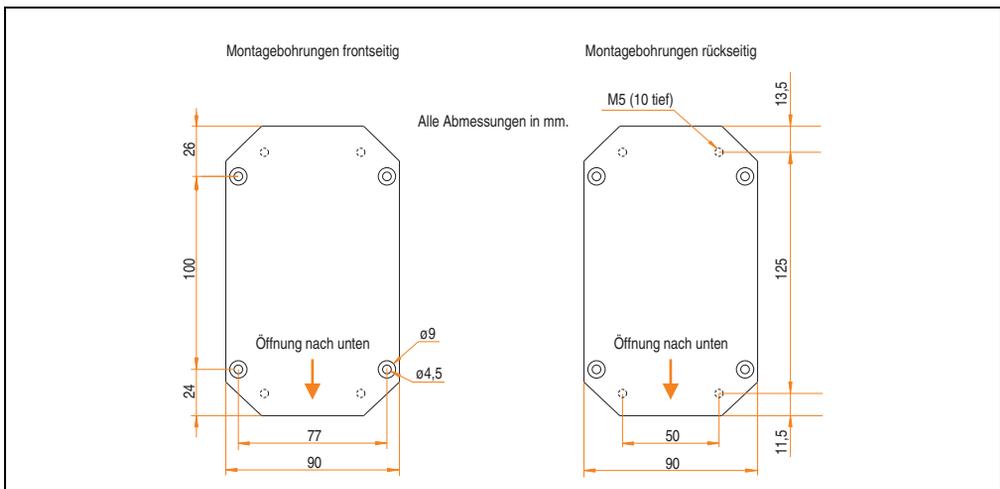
Bohrschablone 4MPCBX.0001-00
